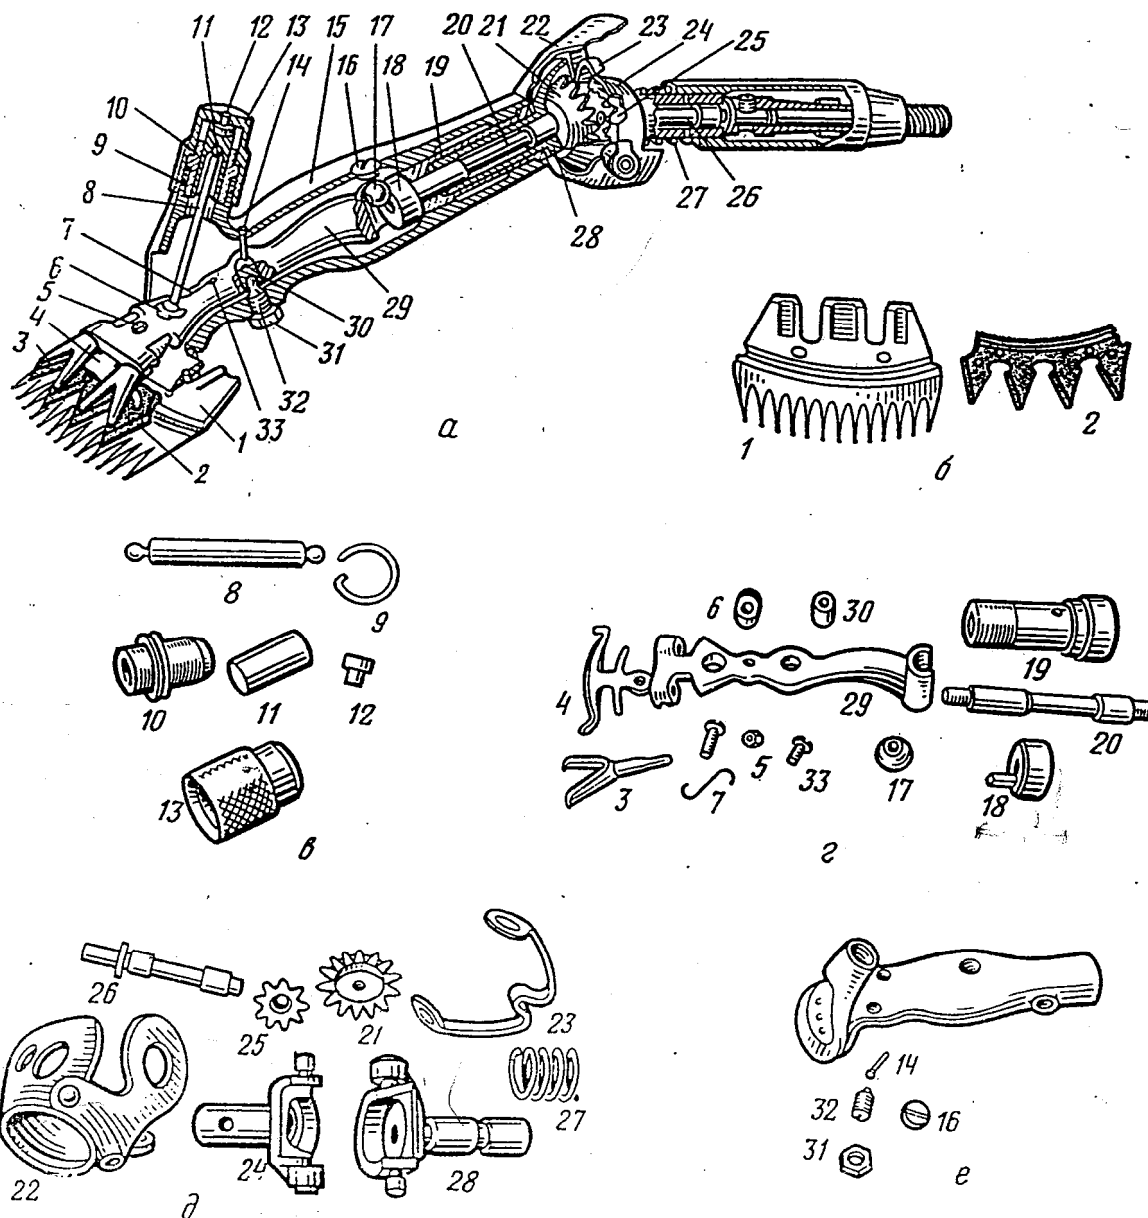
Общий вид (а) машинки МСО-77Б для стрижки овец и детали режущего аппарата (б), нажимного (в), эксцентрикового (г), шарнирного (д) механизмов и корпуса (е): 1 - гребенка; 2 - нож; 3 - нажимная лапка; 4 - пружина нажимных лапок; 5 - гайка; 6 - подпятник стержня; 7, 27 - пружины; 8 - упорный стержень; 9 - стопорная пружина; 10 - штуцер; 11 - нажимной патрон; 12 - упор патрона; 13 - нажимная гайка; 14 - предохранительный винт; 15 - корпус; 16 - заглушка; 17 - ролик; 18 — эксцентрик; 19 - втулка; 20 - валик; 21 - большая шестерня; 22 - наружный кожух; 23 - замок шарнира; 24 - наружный кожух шарнира; 25 - малая шестерня; 26 - передаточный валик; 28 - внутренний кожух шарнира; 29 - рычаг; 30 - подпятник; 31 - контргайка; 32 - центр вращения; 33 - винт
